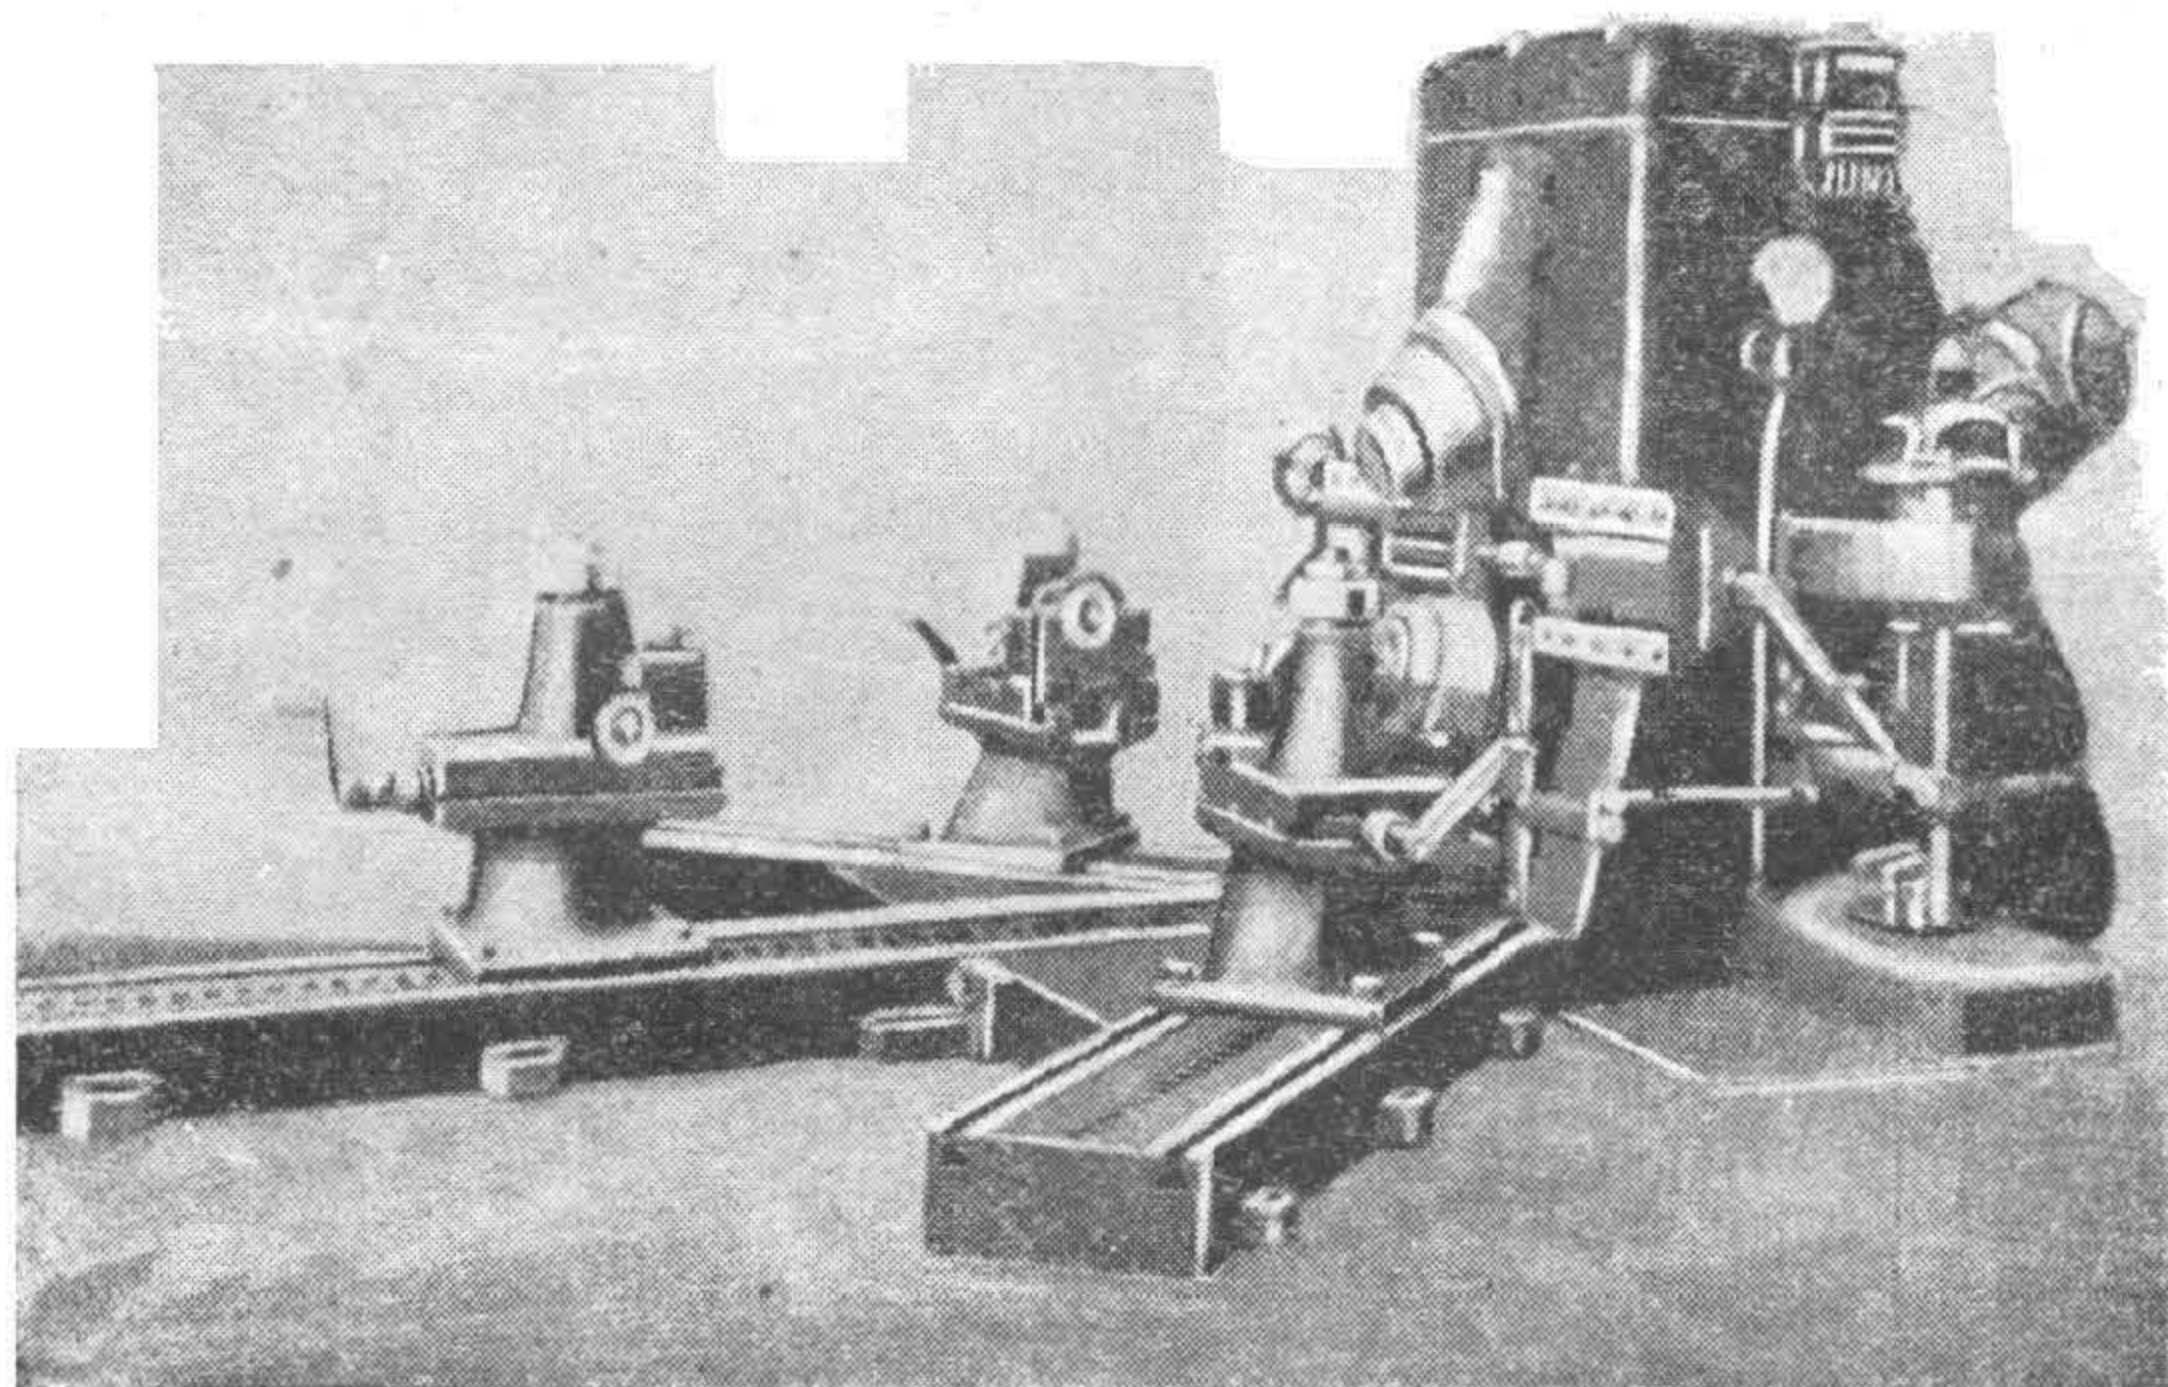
Вальцовочный станок фирмы „Schiss-Defriss“
